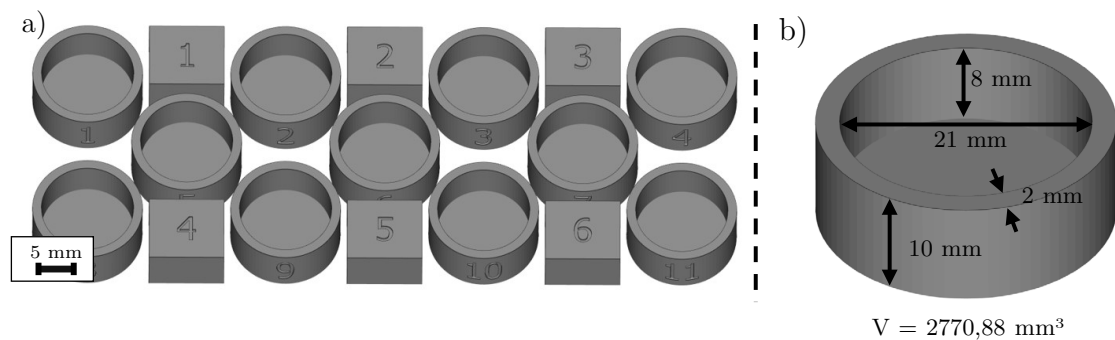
Druckjobdesign (a) und Detailmaße Pulverbettcups (b) [60]
